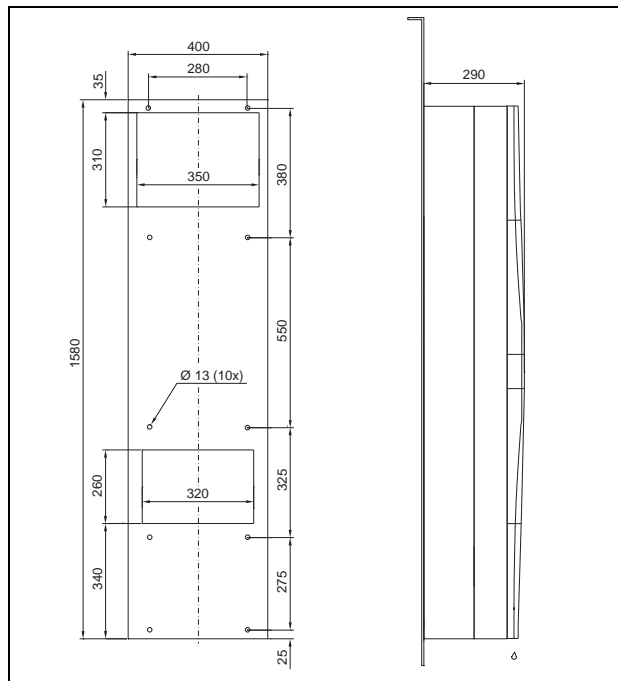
SK 3303.xxx, SK 3361.xxx, pro montáž na povrch
